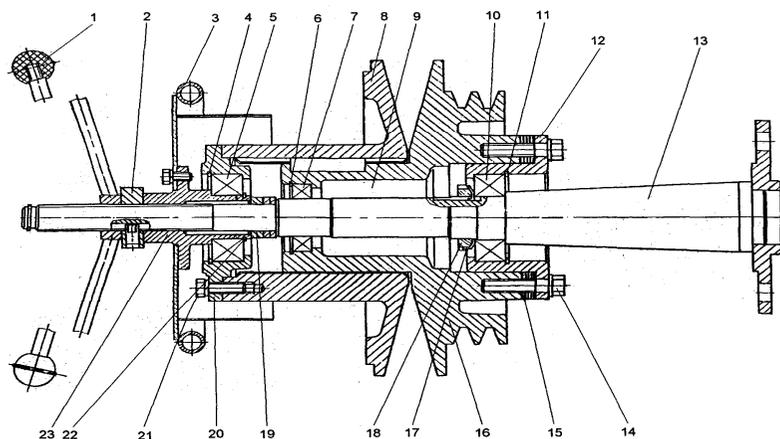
Контрпривод вентилятора: 1 — ручка фиксатора; 2 — стопор; 3 — кожух; 4, 6, 11, 22 — кольца; 5, 7, 10 — подшипники; 8 — диск подвижный; 9 — шпонка; 12 — стакан; 13 — ось; 14, 21 — болты; 15 — прокладки; 16 — диск неподвижный; 17 — шайба; 18 — гайка; 19, 23 — втулки; 20 — корпус
